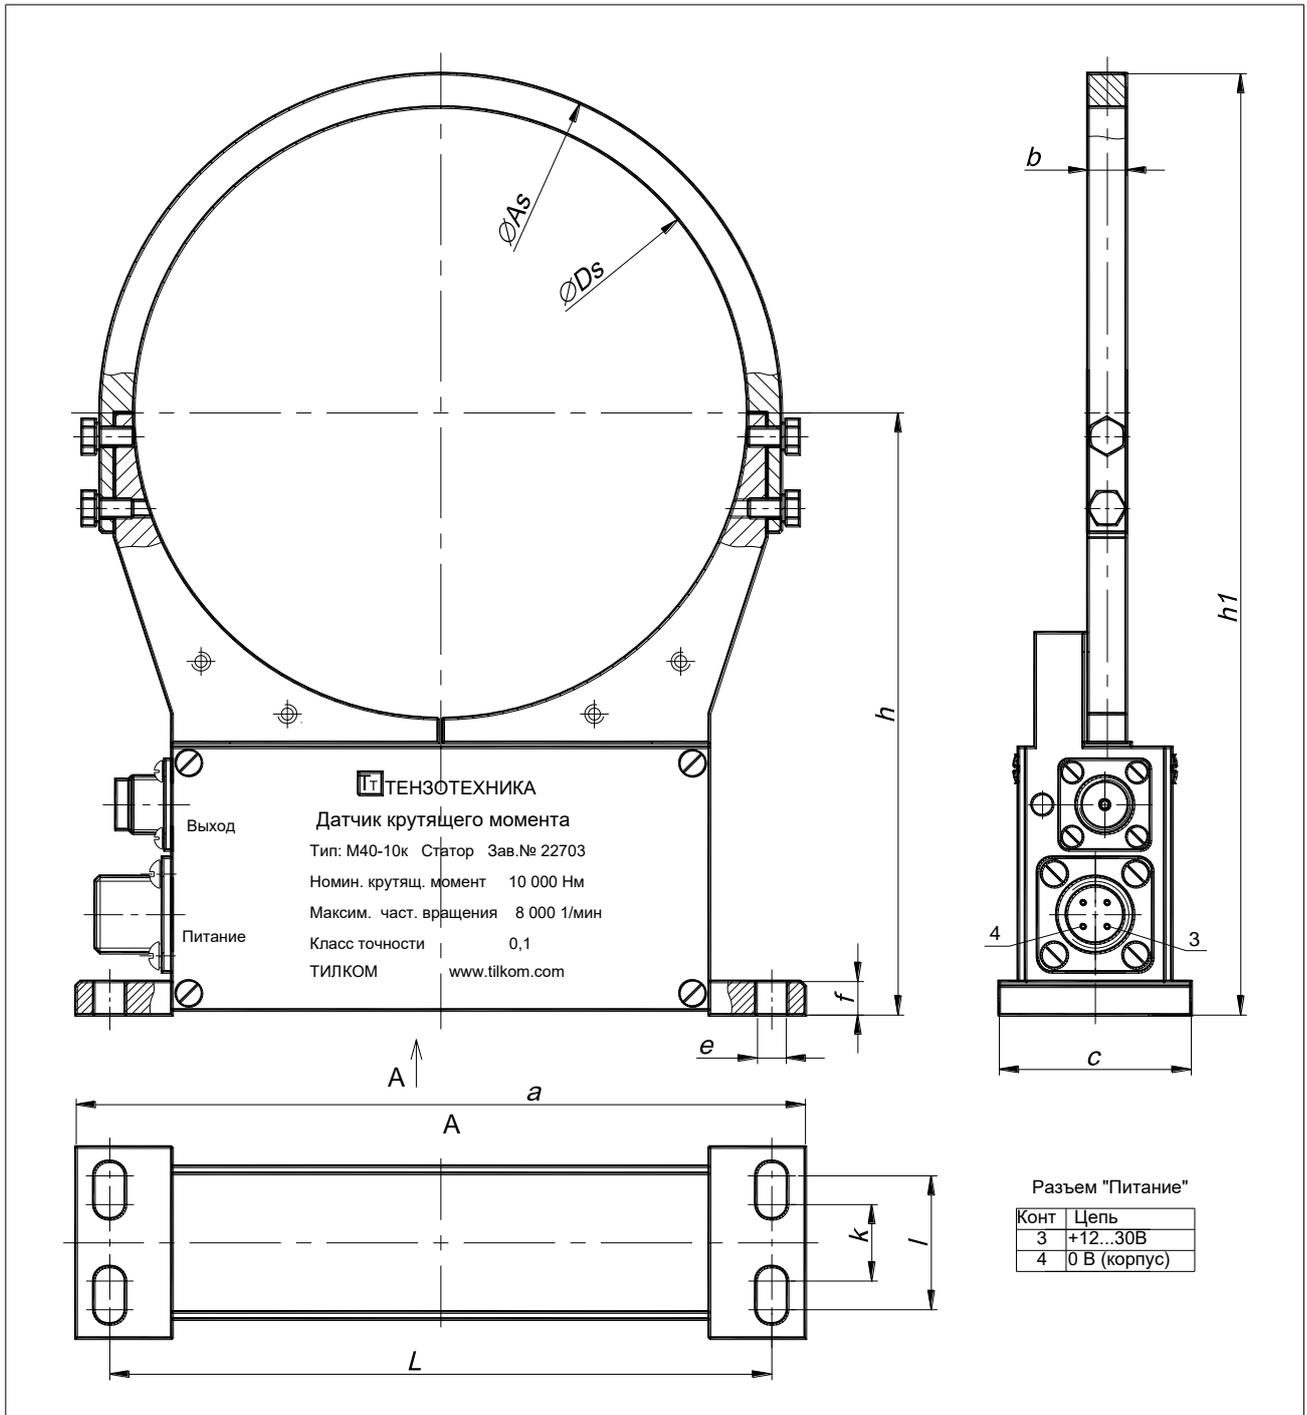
Статор М40-8к... М40-600к. Габаритные и установочные размеры, мм
